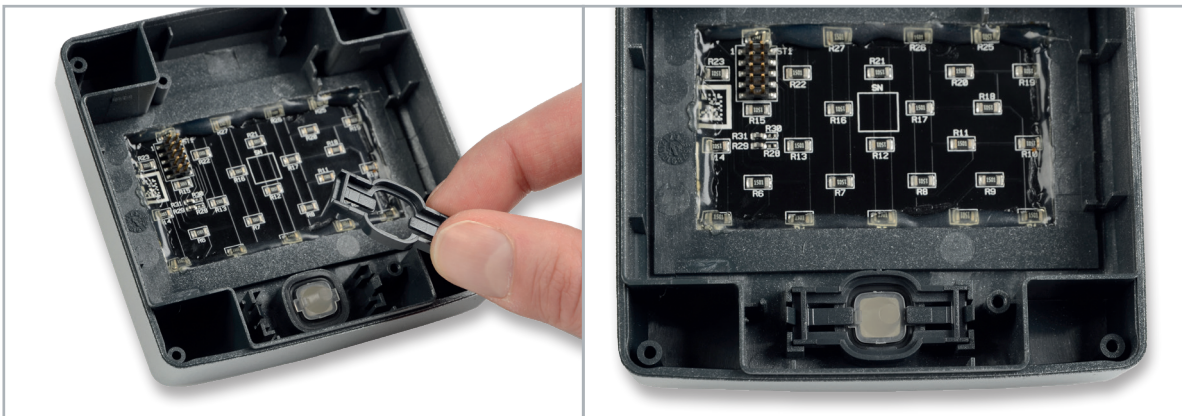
und mit dem Dichtungsanpressstück fixiert.
